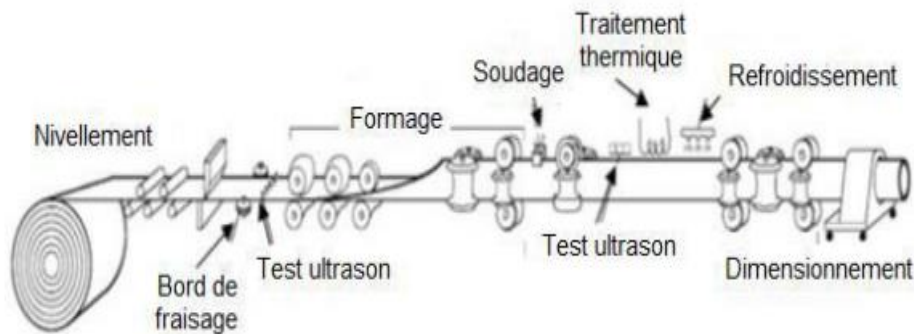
Technique de fabrication des tubes soudés en spirale
